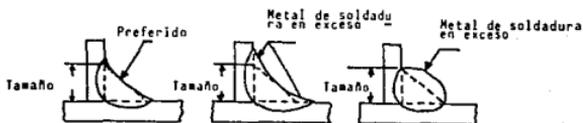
Forma preferida de soldaduras de filete, y el método de medir el tamaño del filete de la soldadura.
